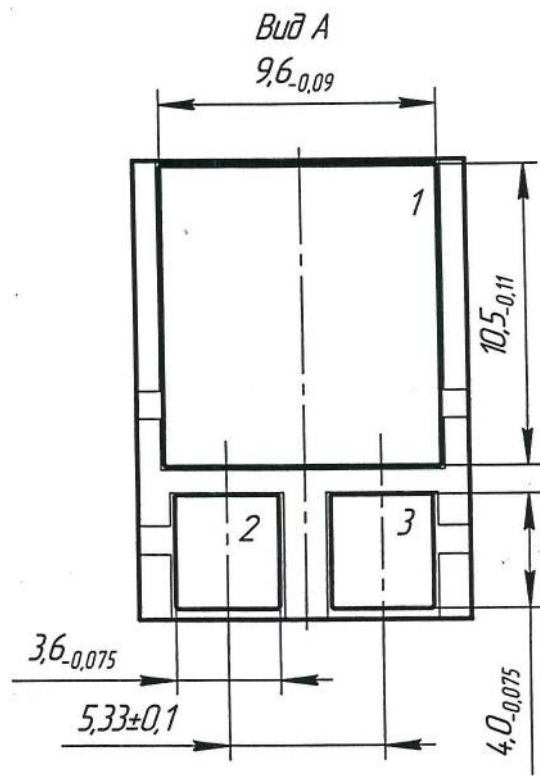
Габаритный чертеж корпуса КТ-94-1
